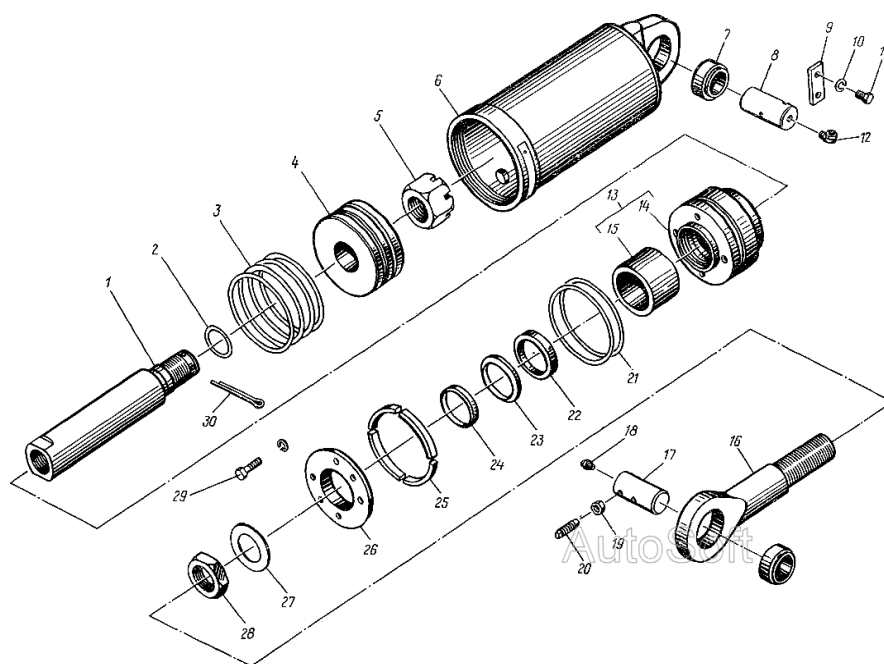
Цилиндр наклона ЛЗА 4014: 1 – Шток, 2 – Кольцо уплотнительное, 3 – Шайба защитная, 4 – Поршень, 5 – Гайка М42х2, 6 – Корпус, 7 – Подшипник шарнирный, 8 – Палец, 9 – Планка стопорная, 10 – Шайба 10, 11 – Болт М10х12, 12 – Масленка П-А-90, 13 – Крышка в сборе, 14 – Крышка, 15 – Втулка, 16 – Головка штока, 17 – Палец, 18 – Масленка I-A1, 19 – Гайка М12х1,25, 20 – Винт стопорный, 21 – Кольцо уплотнительное, 22 – Манжета 71х56-5, 23 – Кольцо защитное 2-56-П, 24 – Грязесъемник Гр 56х66х10х7, 25 – Сектор упорный, 26 – Фланец упорный, 27 – Шайба стопорная, 28 – Гайка М24, 29 – Болт М10х35, 30 – Шплинт 8х80.
